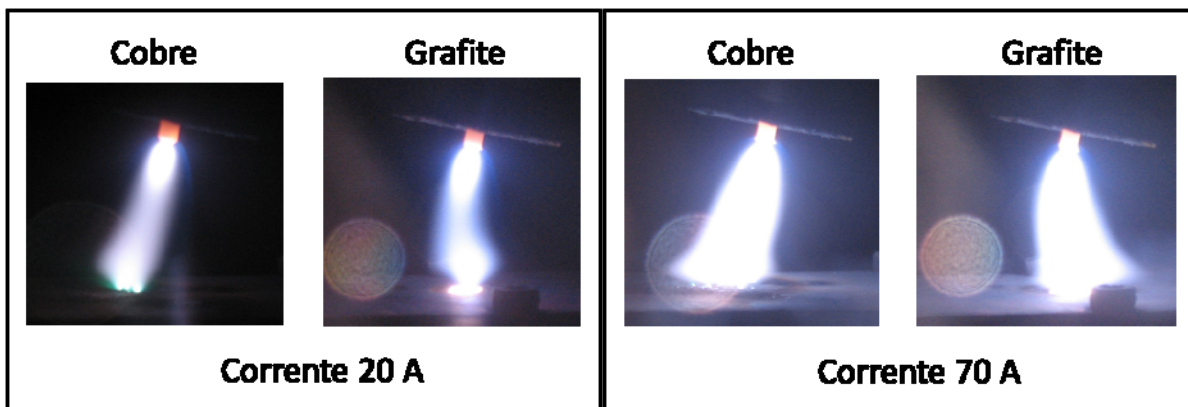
Imagem do arco de soldagem TIG com corrente muito baixa (20 A) e corrente já utilizada em soldagem e comprimento de 17 mm.
